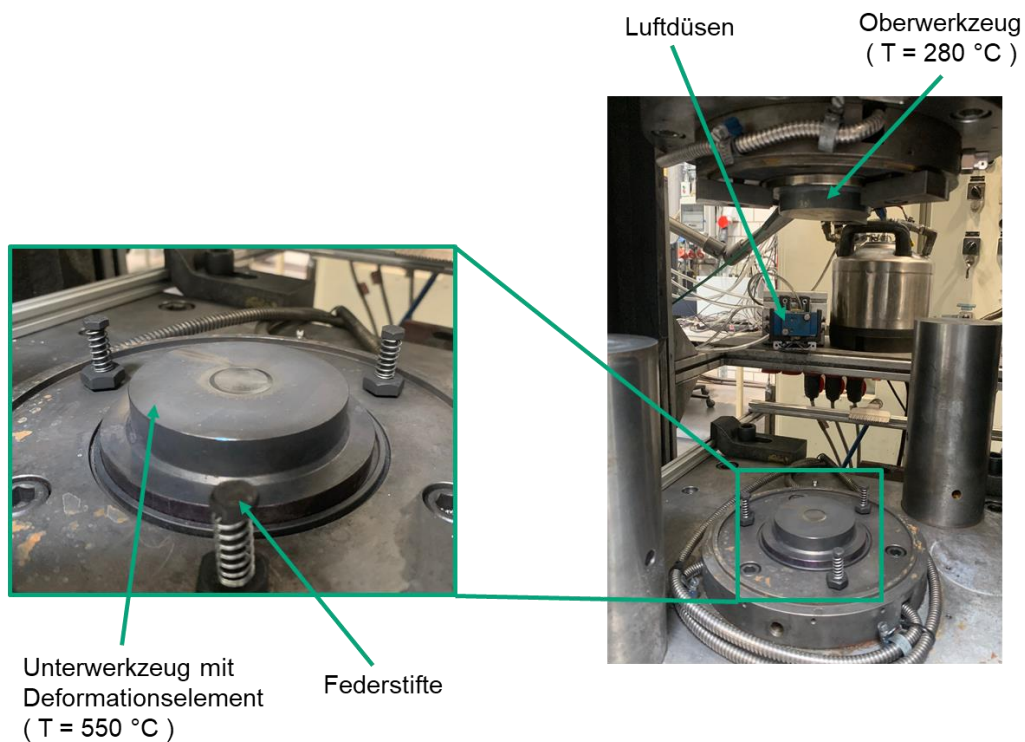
Pressenraum der Spindelpresse mit eingebauten Werkzeugen
